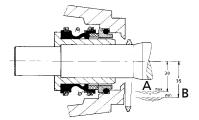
Llenado de la precámara de aceite - Montaje horizontal
